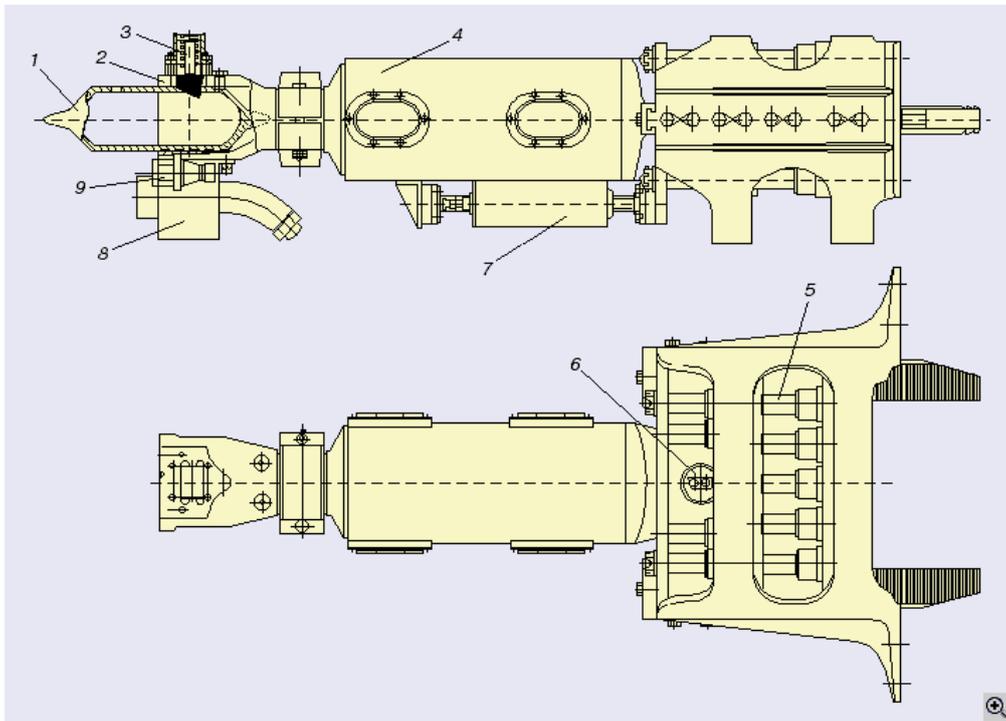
Автосцепное устройство высокоскоростного электропоезда «Сокол»: 1 — съемный направляющий элемент; 2 — корпус; 3 — механизм сцепления (замок); 4 — поглощающий аппарат; 5 — блок аварийных амортизаторов; 6 — шарнирный узел со сферическим подшипником; 7 — эластичное центрирующее устройство; 8 — автосоединитель электрических магистралей; 9 — автосоединитель воздушных магистралей
